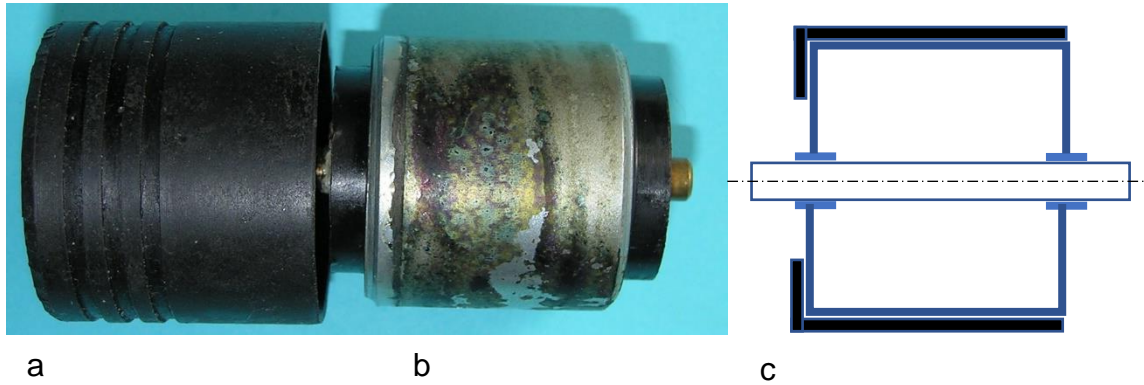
Union-Seitendynamo: a) Gummizylinder, b) Oberfläche des Magnetjochs, c) Skizze zur Position Gummizylinders
